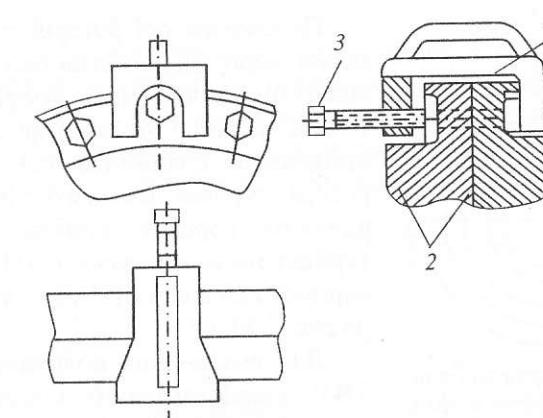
Пристрой для випресування з'єднувальних болтів муфти:
